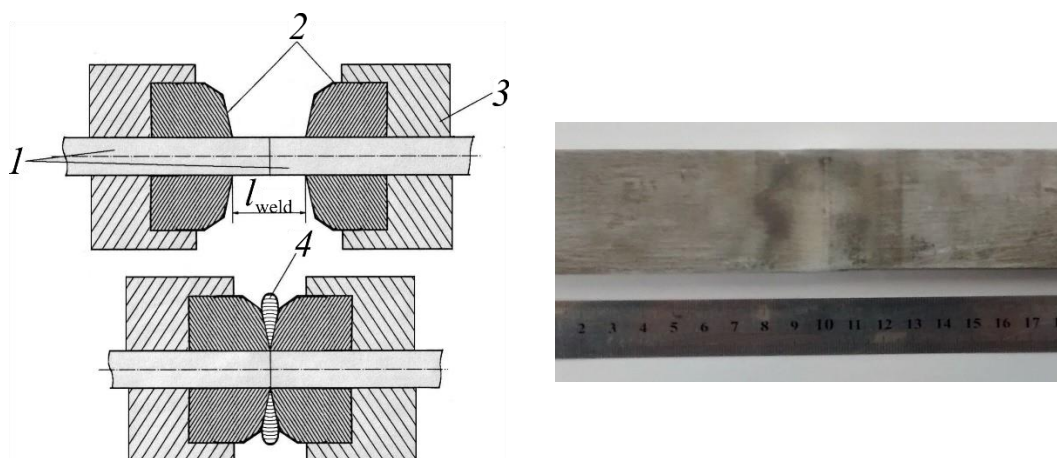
Схема контактной стыковой сварки с формированием соединения: 1 – детали; 2 – формирующие устройства; 3 – токоподвод; 4 – экструдированный металл; l_{weld} – припуск на сварку
